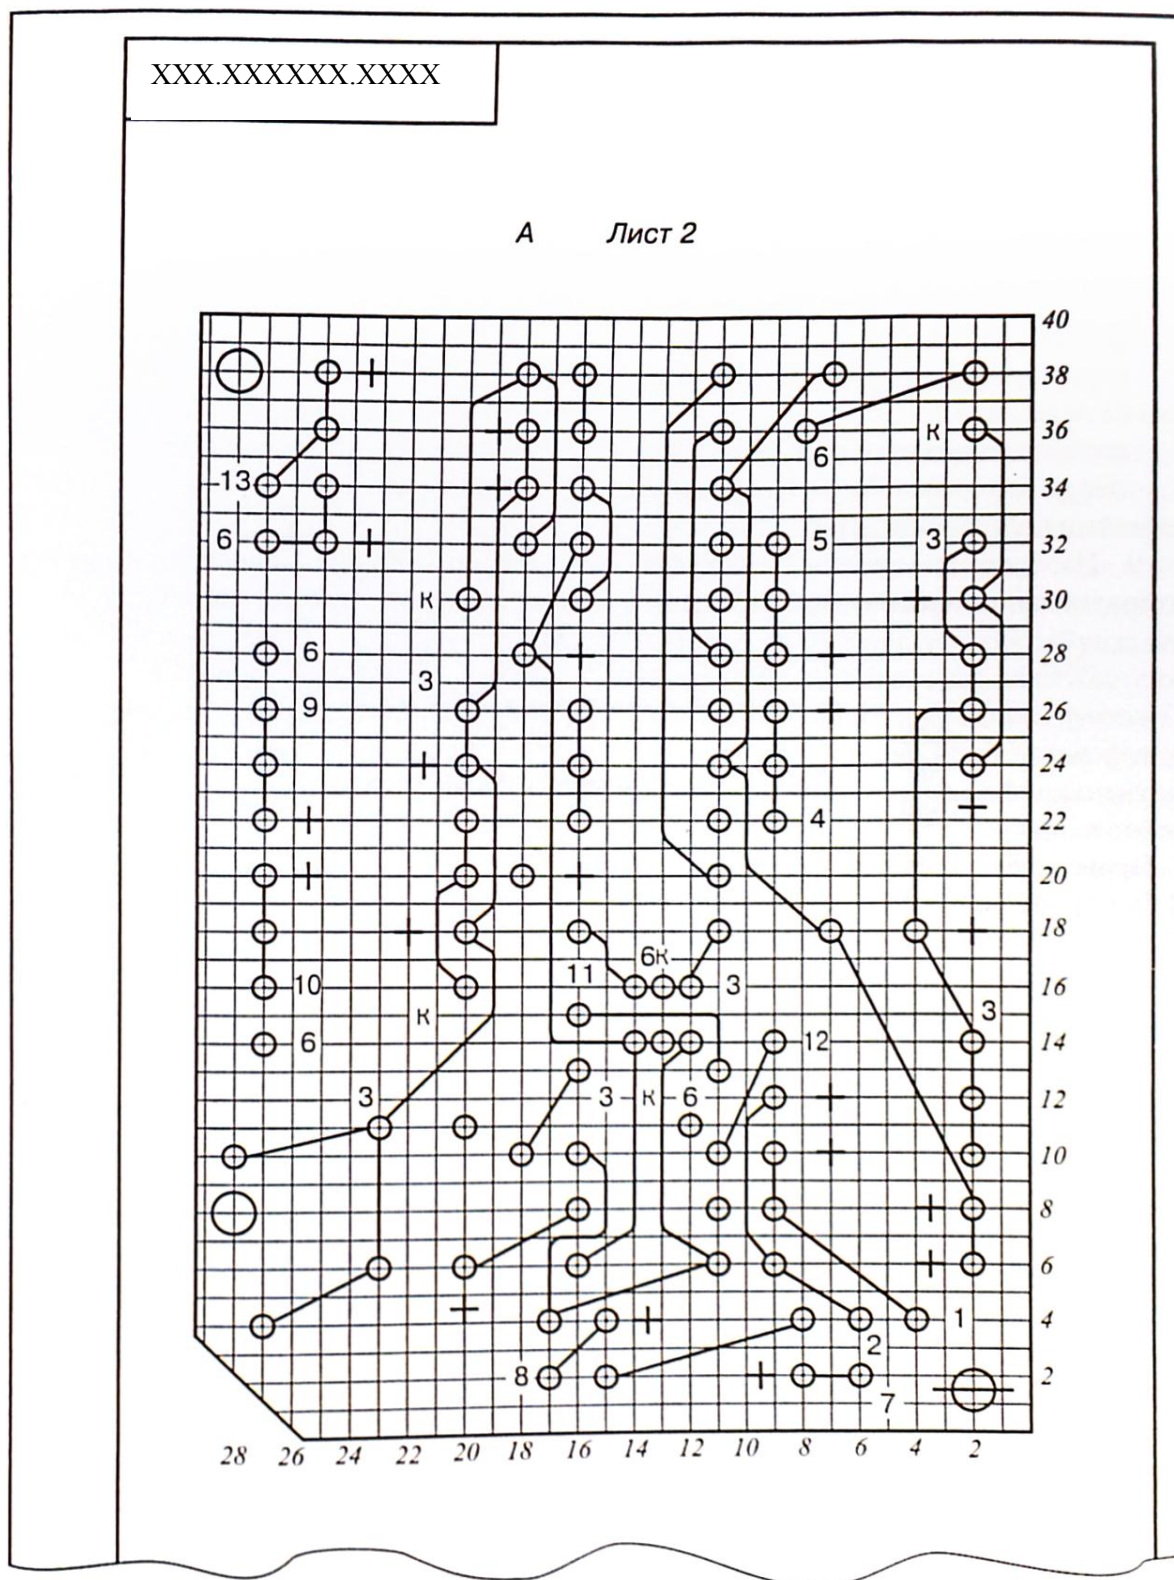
Пример чертежа двухсторонней печатной платы
